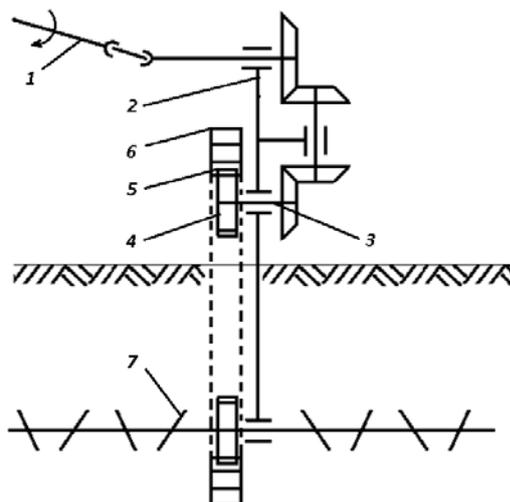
Кинематическая схема разработанной машины: 1- вал отбора мощности, 2- корпус орудия, 3- передаточные шестерни, 4- приводная шестерня, 5- зубчатое зацепление, 6- дисковая фреза. (составлено авторами)
